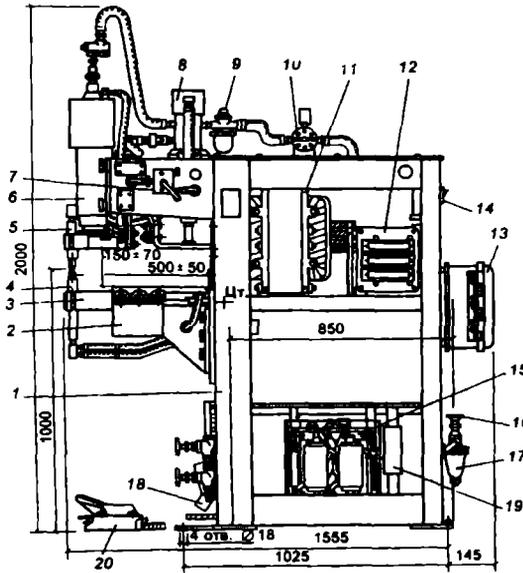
Машина МТ-1610 для точечной сварки:
